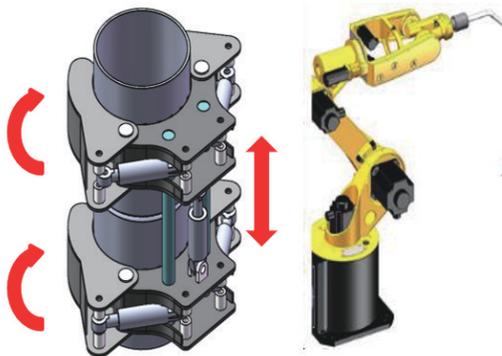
套管快速夹紧对中装置及全自动焊接机器人
